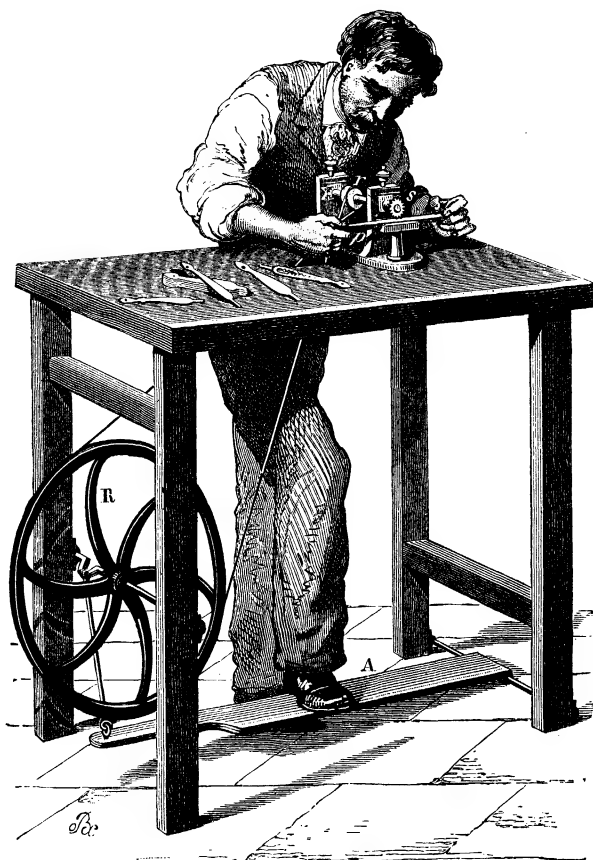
Fräsmaskin för tillverkning af solfjädrar.
